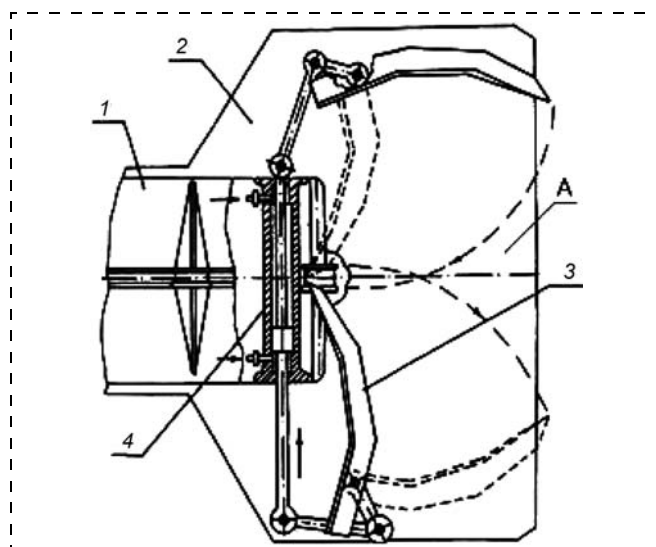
Погрузочный орган с клиновыми поворотными лапами: 1 — конвейер; 2 — наклонный питатель; 3 — нагребавшие лапы; 4 — двухштоковый гидроцилиндр
